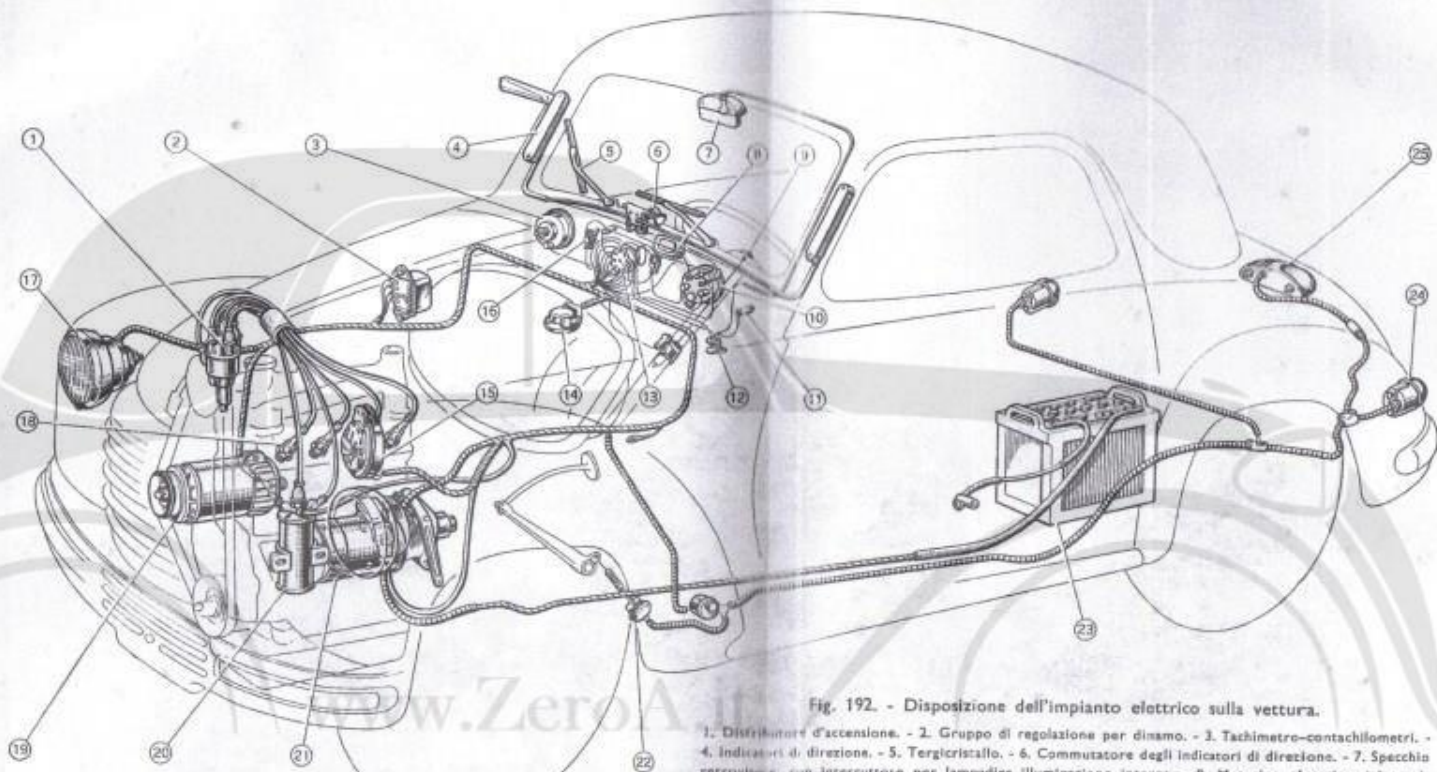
Disposizione dell'impianto elettrico sulla vettura.
